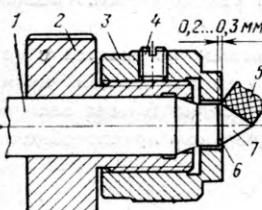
Приспособление для шлифования (обнижения) нерабочей части конуса иглы:
